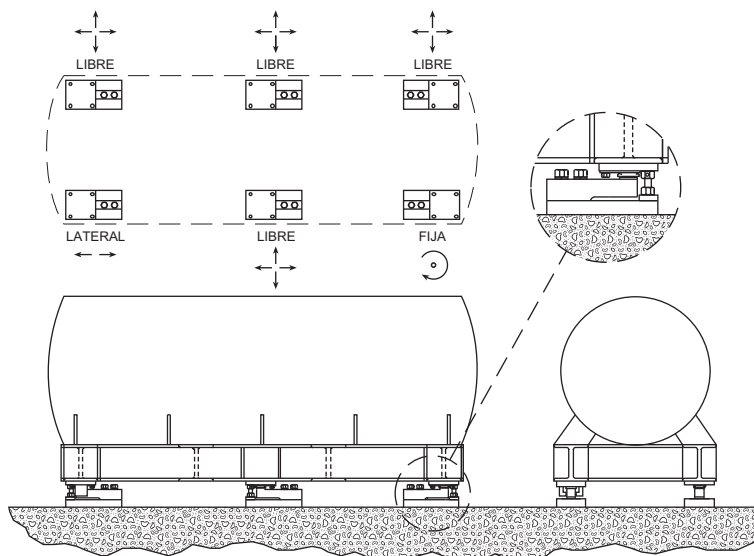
Sistema de Montaje Paramounts en Tanque Cilíndrico
